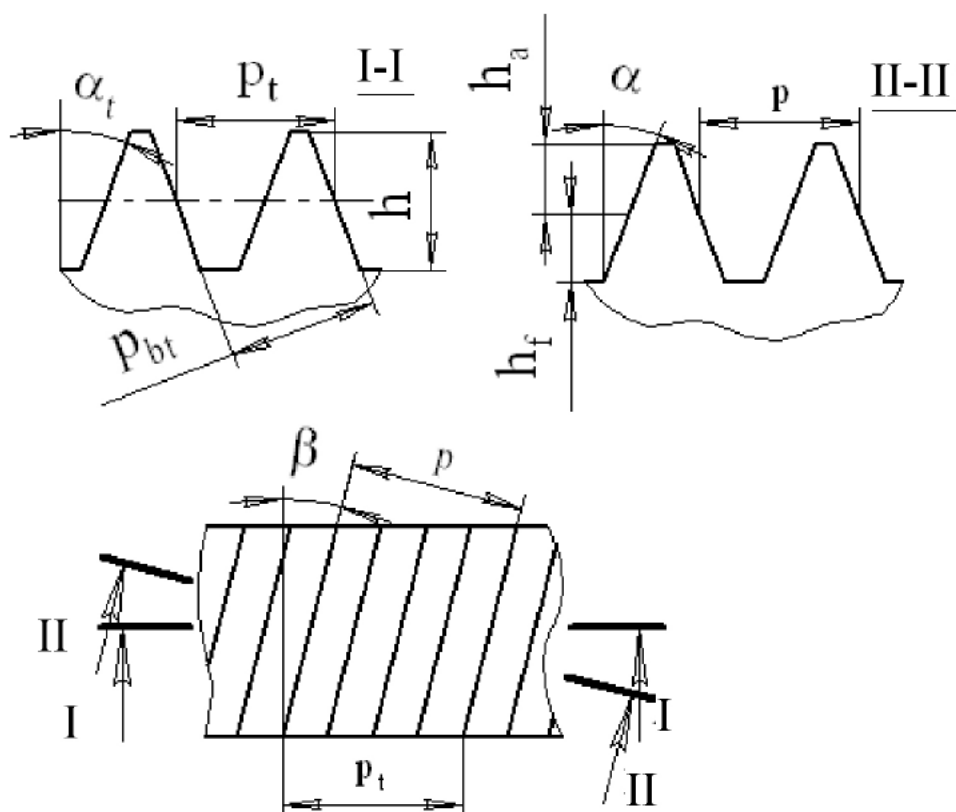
Стандартный исходный контур инструмента реечного типа:
